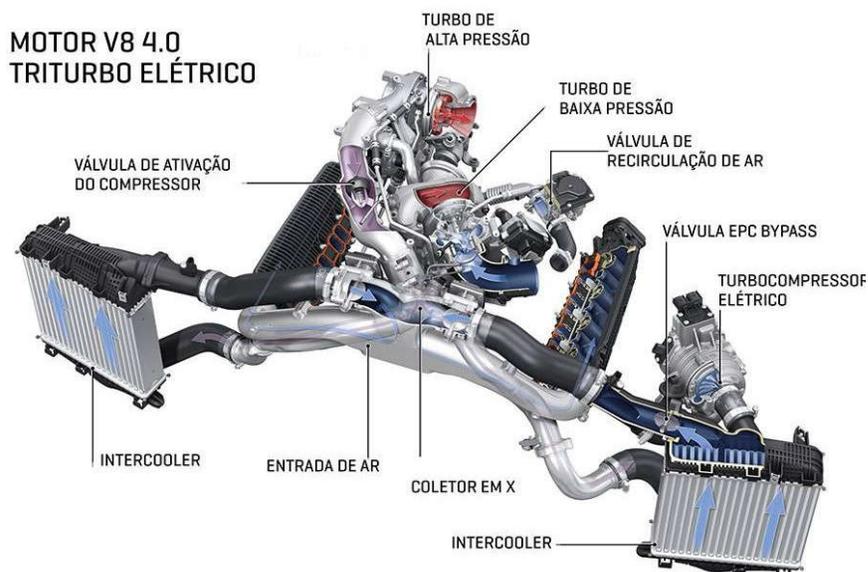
; sistema de compressão e turbos motor v8 AUDI.
